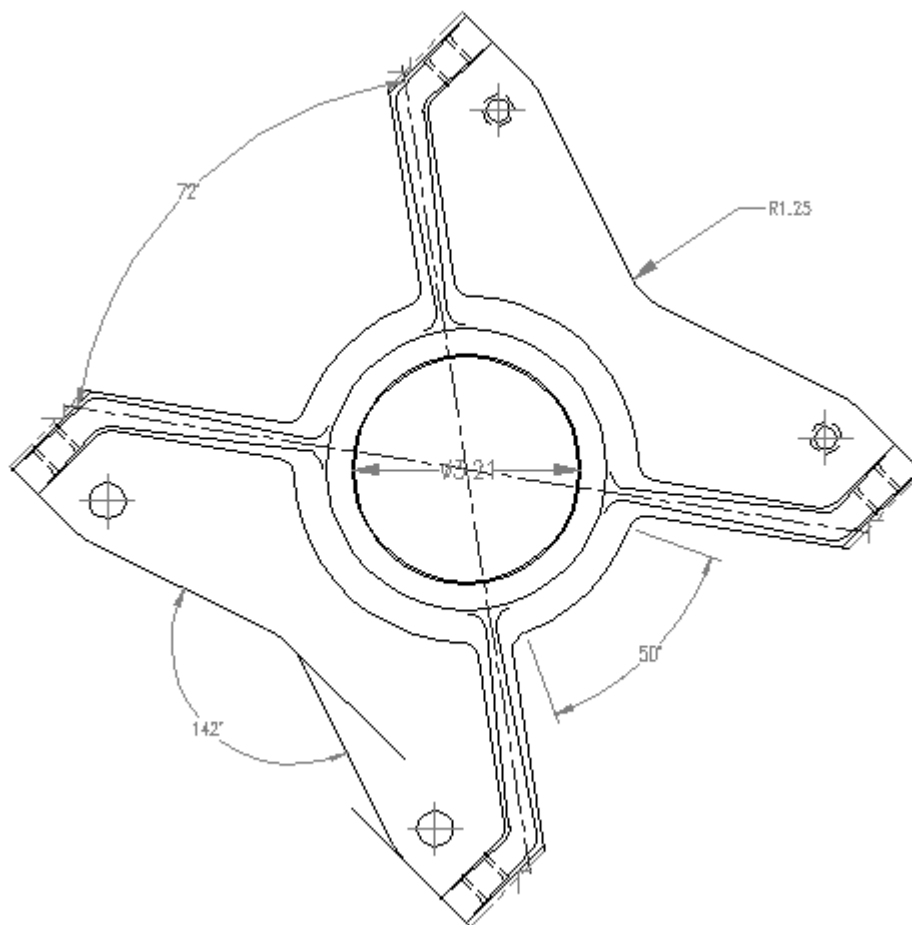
Радиальные и угловые размеры (корпус подшипника)
